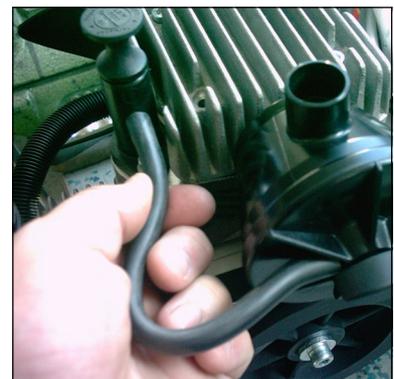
Entlüftungsschlauch am Öleinfüllstutzen montieren
